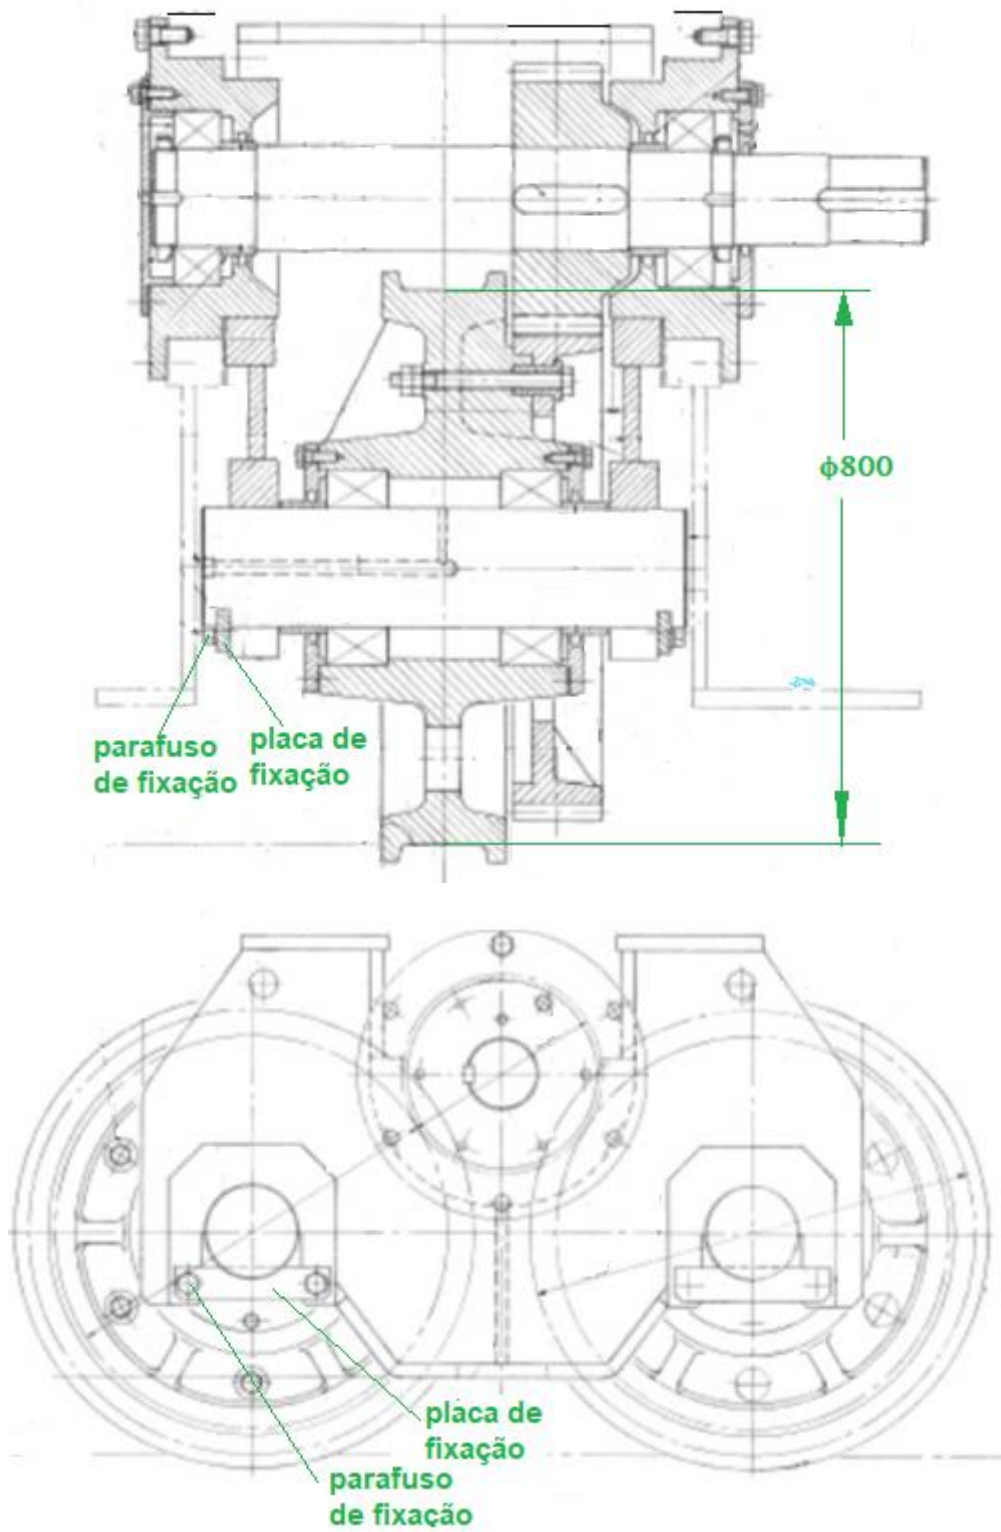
Conjunto de rodas motoras com o sistema externo de engrenamento nas rodas.
